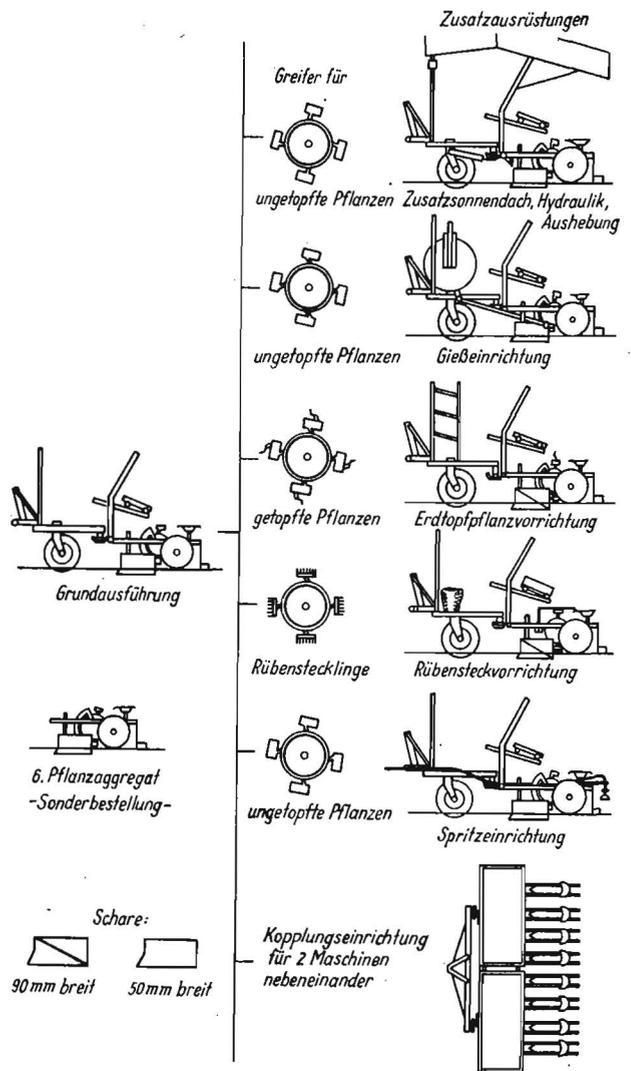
Übersichtsschema der Pflanzmaschine A 832
